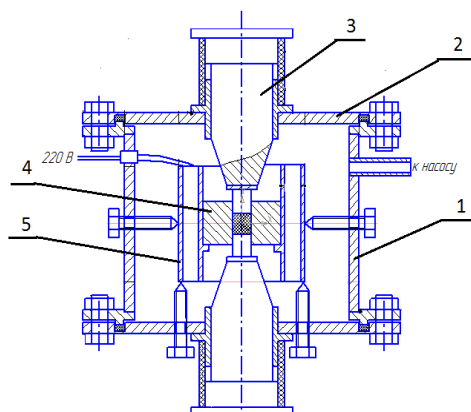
Общий вид вакуумной камеры: 1 – корпус; 2 – крышка; 3 – толкатель; 4 – пресс-форма; 5 - печь
